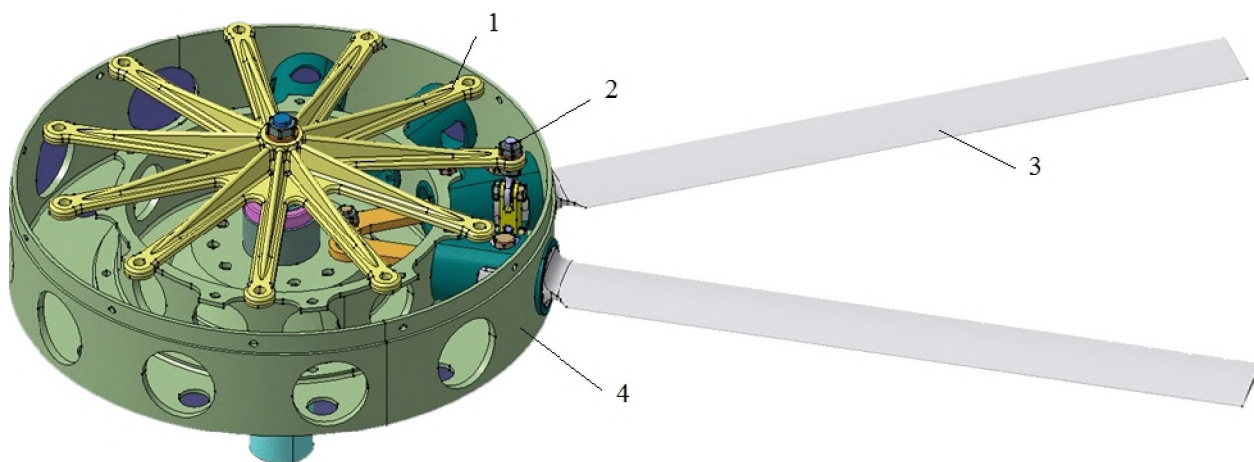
Конструкция корпуса втулки РВ типа "винт в кольце":
